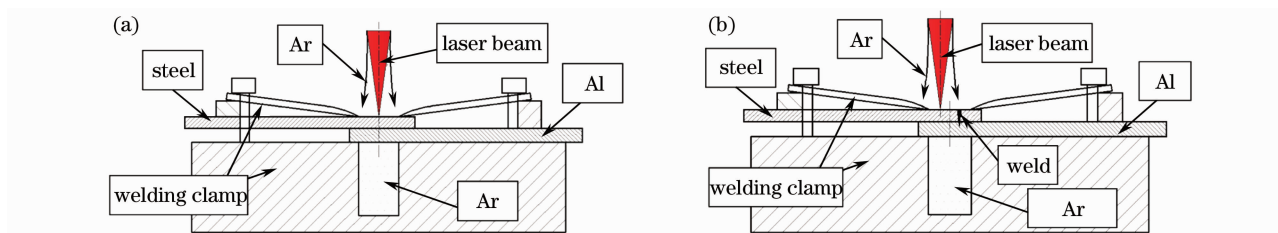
焊缝布置形式示意图。(a)单焊缝,(b)双焊缝
